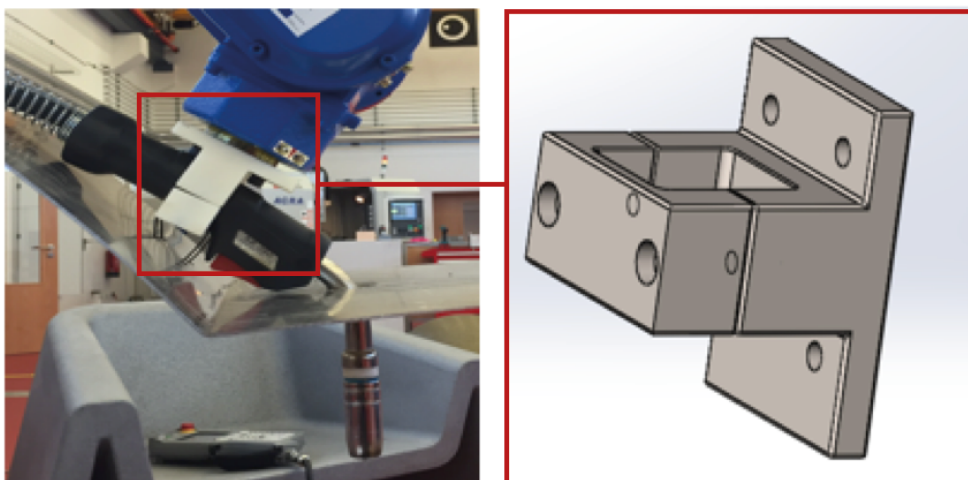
Pormenor do acoplamento entre a tocha de soldadura e o braço robot
